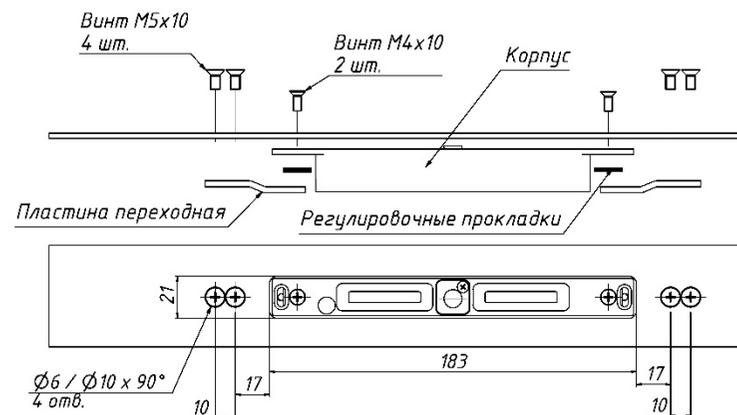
Установка корпуса замка в металлическую дверную коробку
